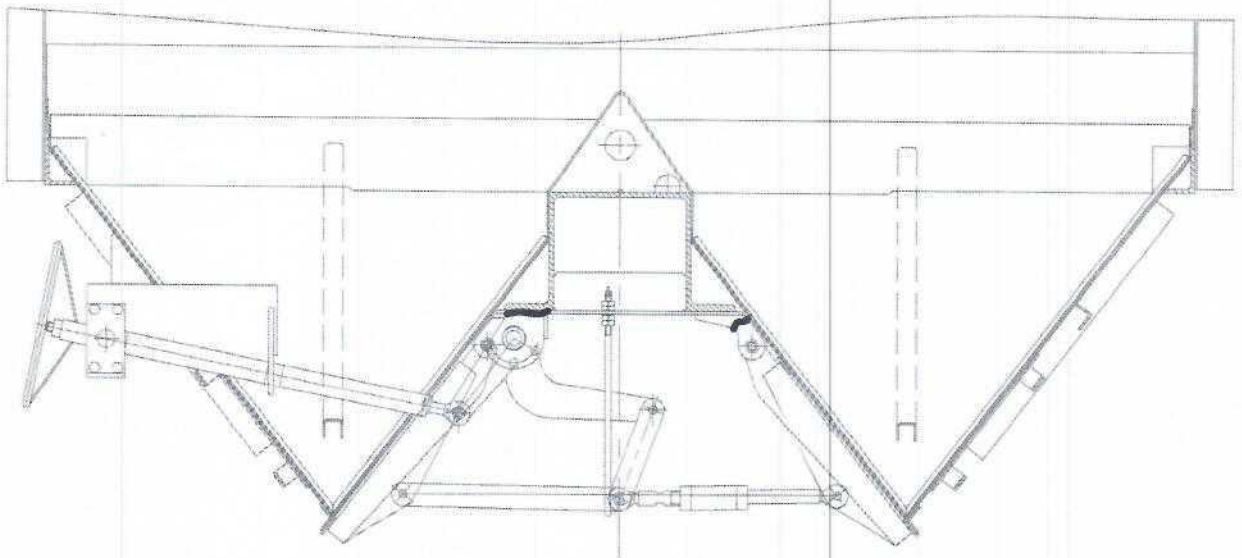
Трещины крепления крышки разгрузочного люка
